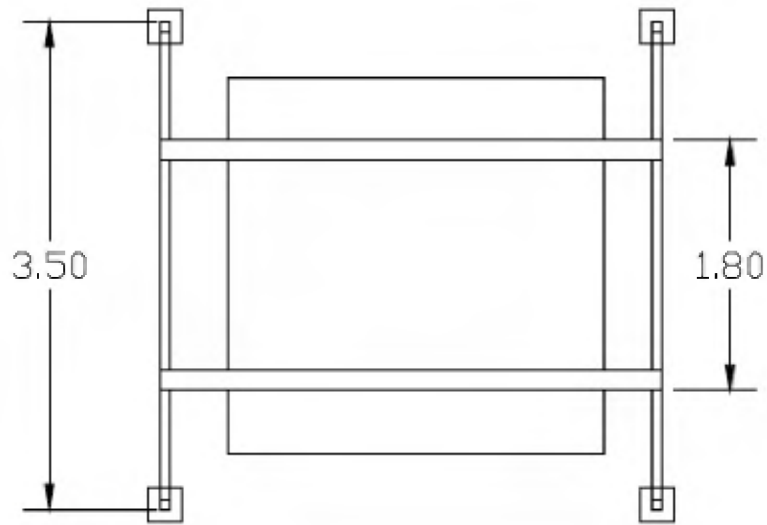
Vista superior de la estructura del sistema de movilización de la compuerta del horno
